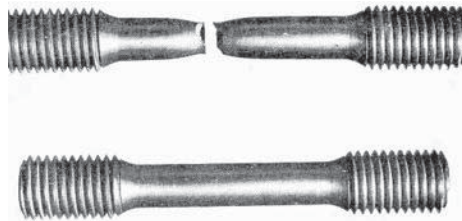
Probetas para el ensayo de tensión ⁽²⁷⁾
